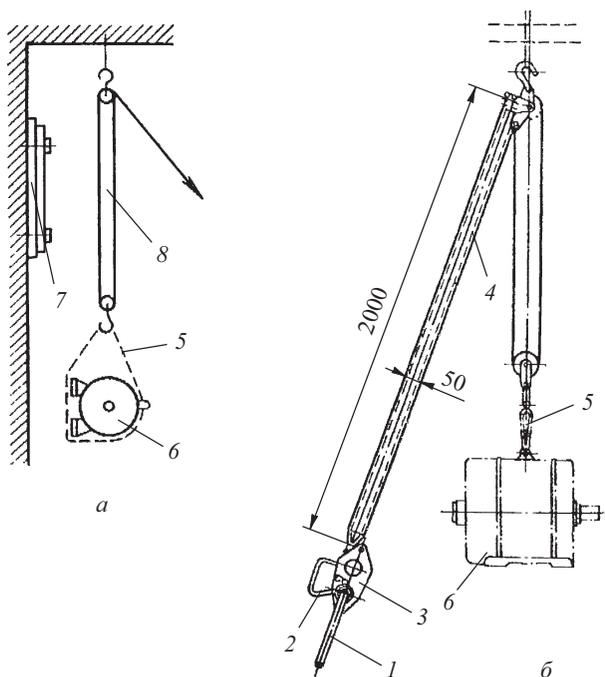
Установка электродвигателей с помощью ручных приспособлений:
